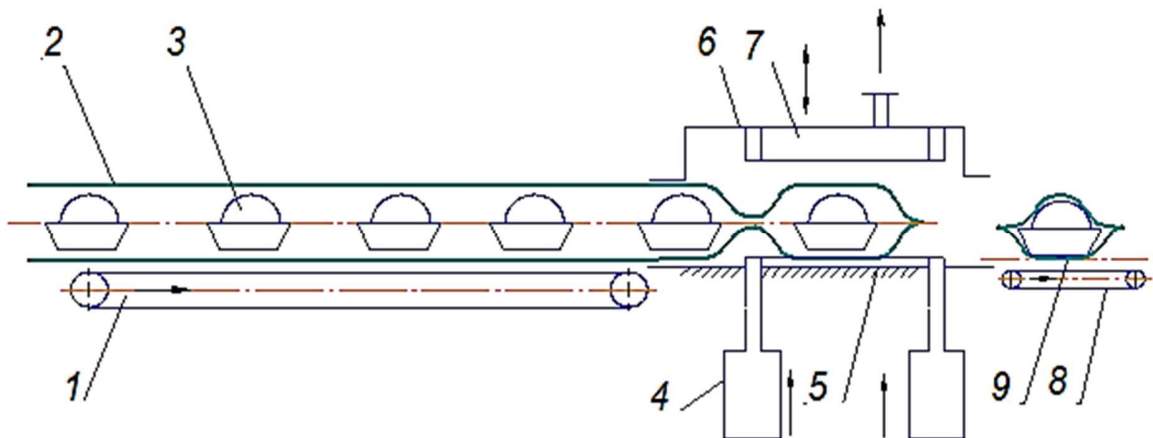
Схема вакуумного пакування: 1 – подавальний конвеєр; 2 – U-подібна плівкова заготовка; 3 – упаковані порції; 4, 7 – зварювальні ножі; 5 – вакуумний пристрій; 6 – кришка, що герметизує; 8 – відвідний конвеєр; 9 – готовий упакований виріб
